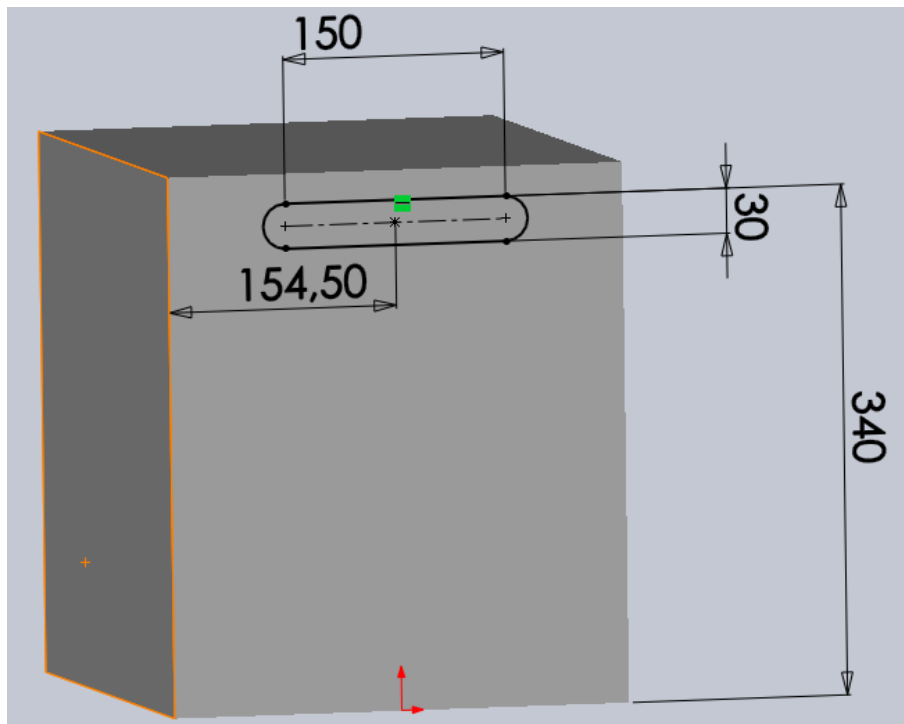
Dimensiones y posición de la ranura. Fuente propia.
